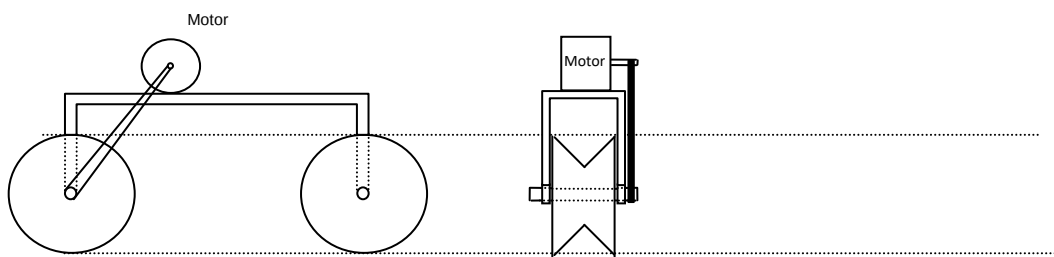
Vista frontal e lateral do suporte superior para o motor
